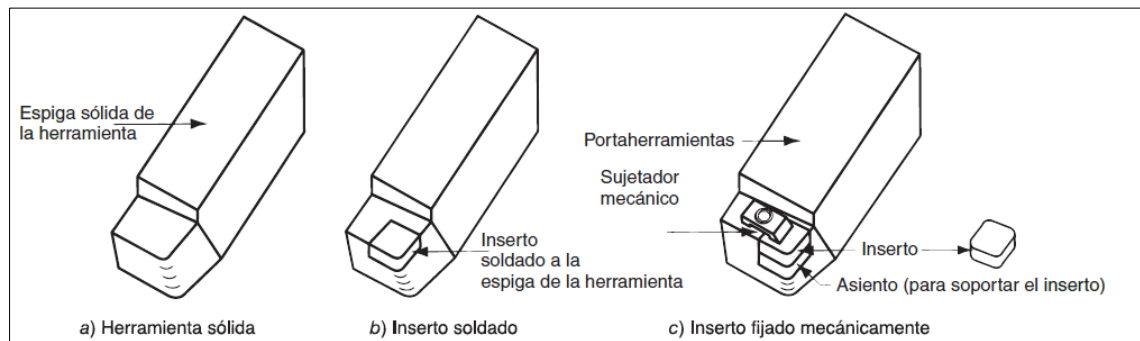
Formas para sostener y presentar el borde de corte de una herramienta
